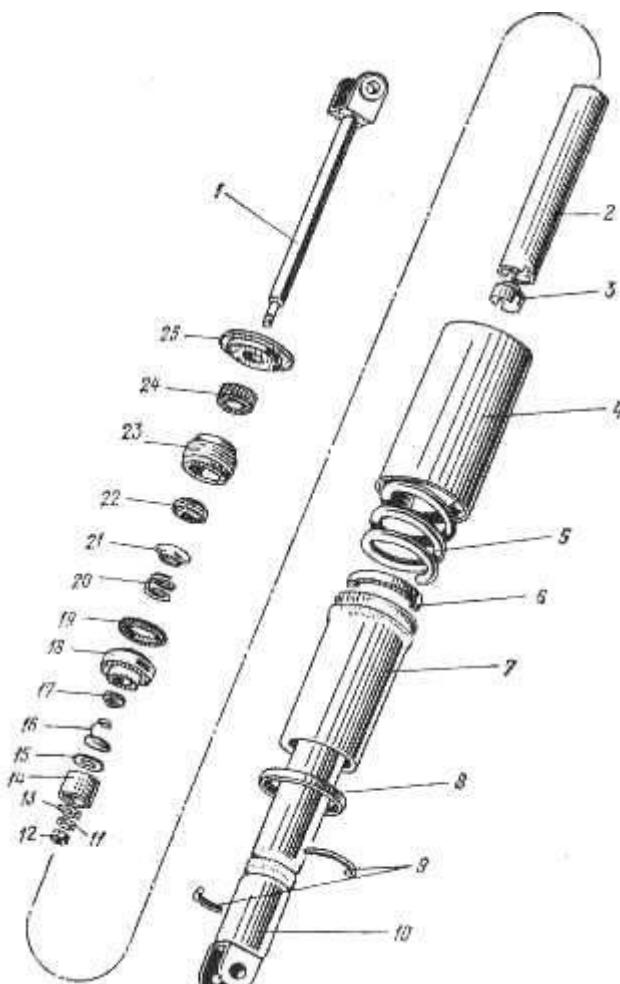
Детали пружинно-гидравлического амортизатора задней подвески:
